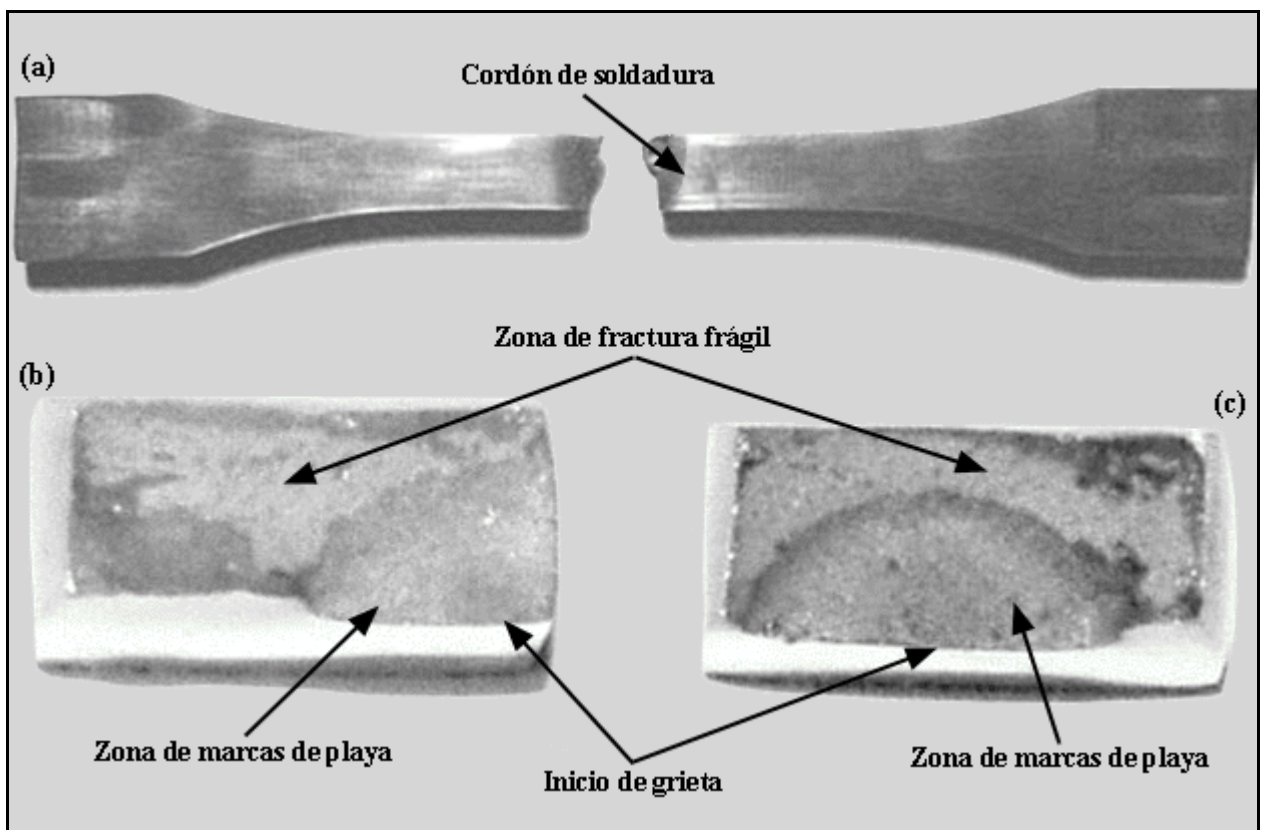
(a) Vista de la fractura de la probeta de fatiga # 4 de la junta soldada; (b) y (c) Secciones transversales de la fractura de las probetas de fatiga # 4 y 8 respectivamente.
